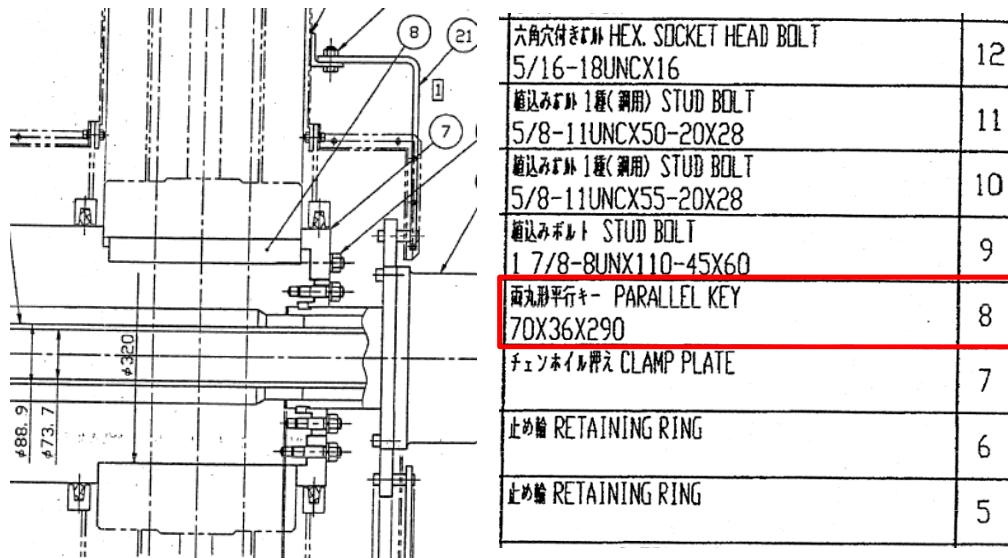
Indicación de la chaveta en los planos del secador.
